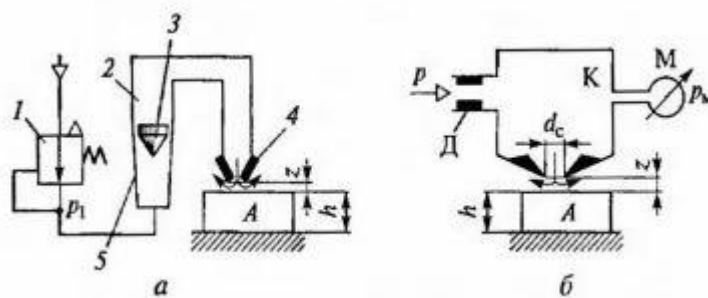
Схемы пневматических систем контроля размеров: а - ротаметрической; б - манометрической; 1 - редукционный пневмоклапан; 2 - расходомер; 3 - поплавок; 4 - сопло; 5 - конусная труба
